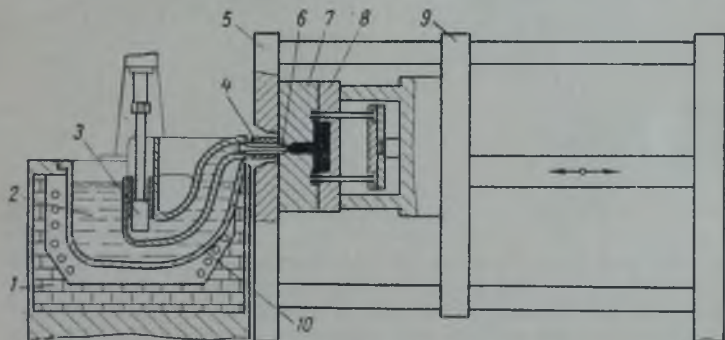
Схема машины для литья под давлением с горячей камерой прессования:
